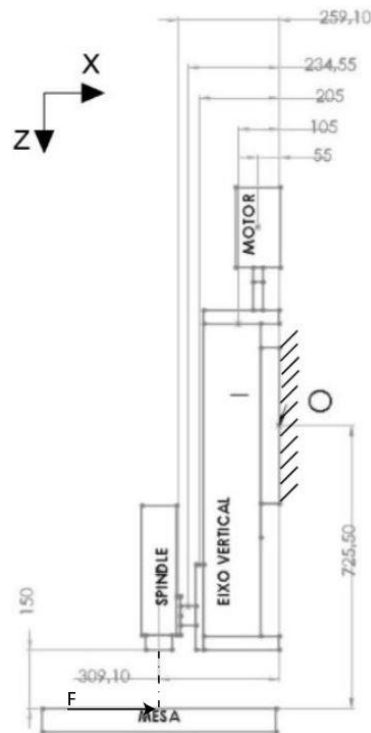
Esquema simplificado da montagem do eixo vertical MKK165 (dimensões em mm)
